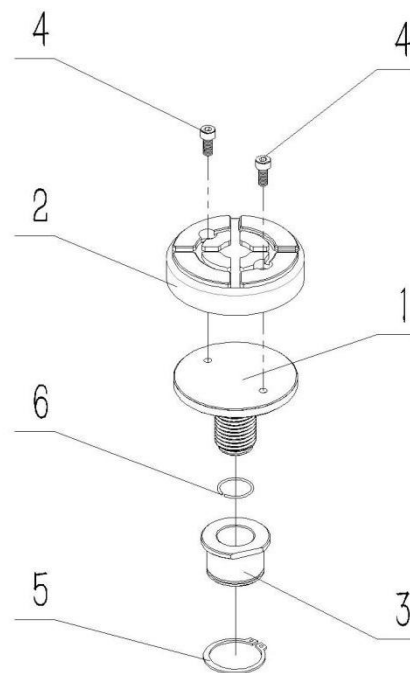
Explosionszeichnung des Hebebock-Palettenbauteils
